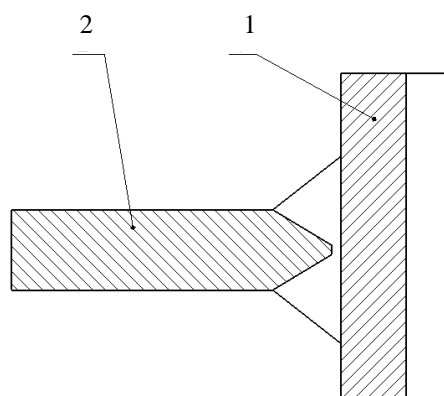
Сечение сварного соединения типа «штуцер — лист»: 1 — штуцер; 2 — лист (оболочка)
